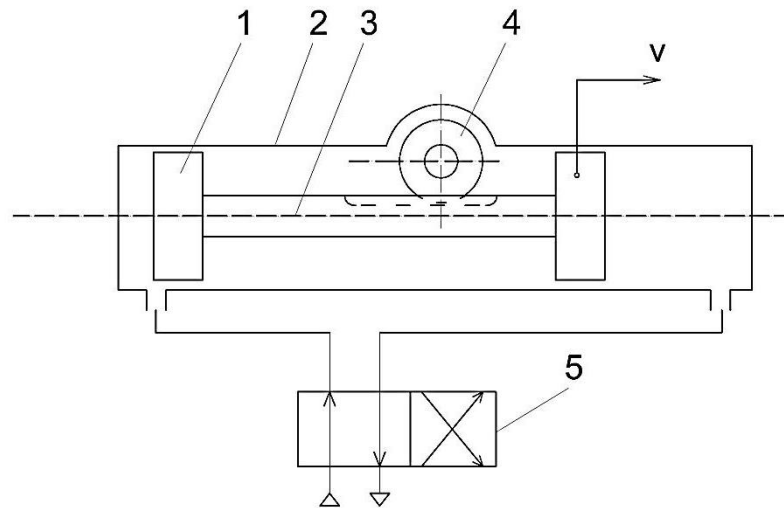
Схема поворотного пневмоприводу ПР: 1 – поршень; 2 – пневмоциліндр двосторонньої дії; 3 – шток-рейка; 4 – зубчасте колесо; 5 – повітроділильник
